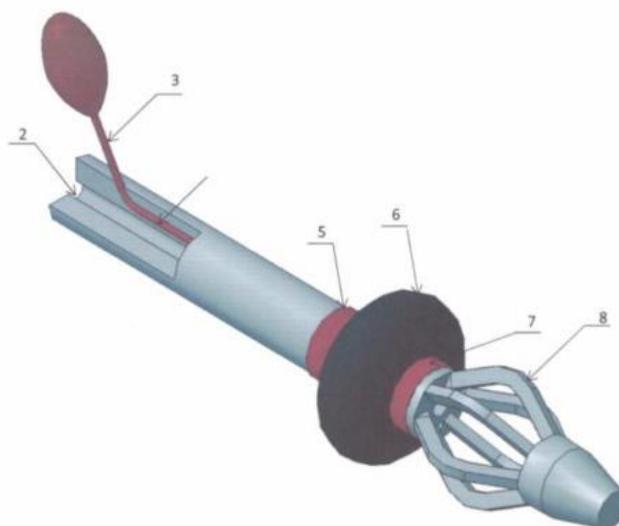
Внешний вид разработанного устройства в сборе.
